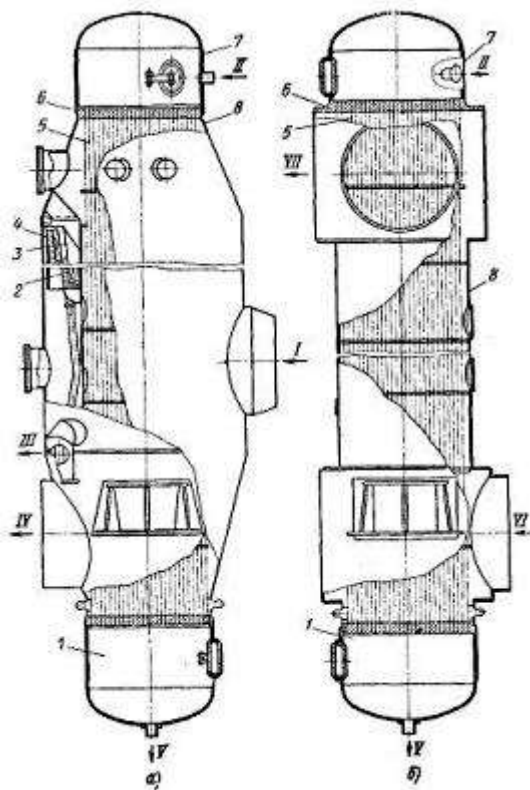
Гладкотрубный сепаратор-пароперегреватель:
